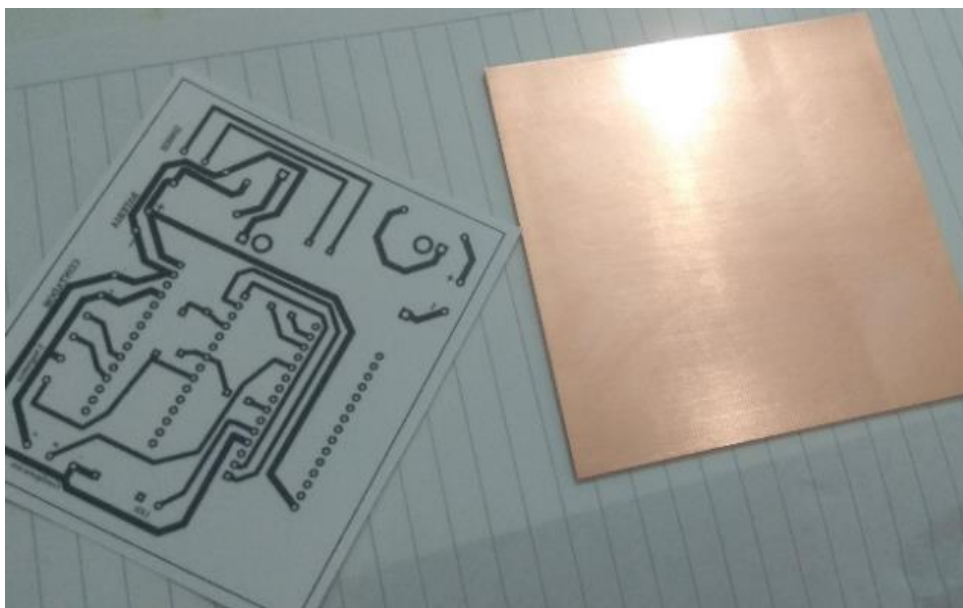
Diseño impreso, junto a la placa antes de ser transferida
